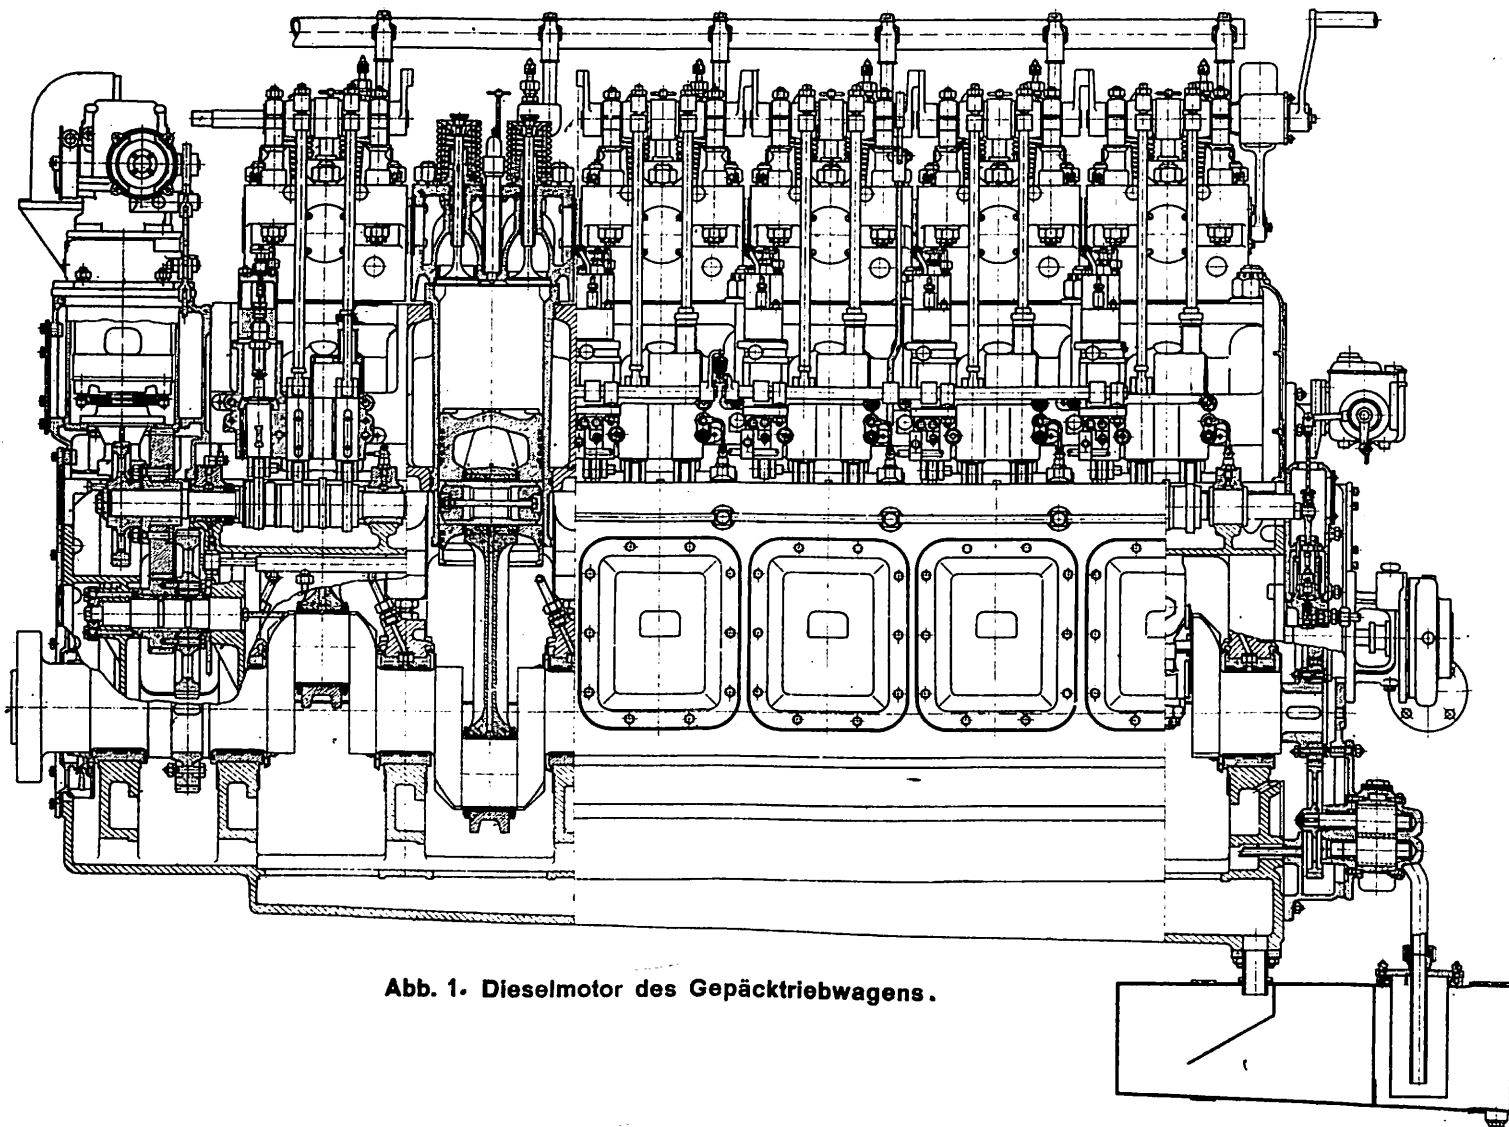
Dieselmotor des Gepäcktriebwagens.
